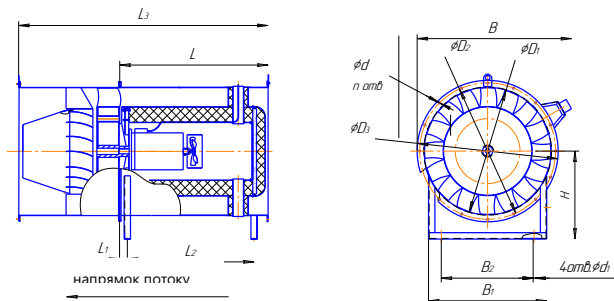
Габаритні креслення вентилятора типу AF-DU-04
